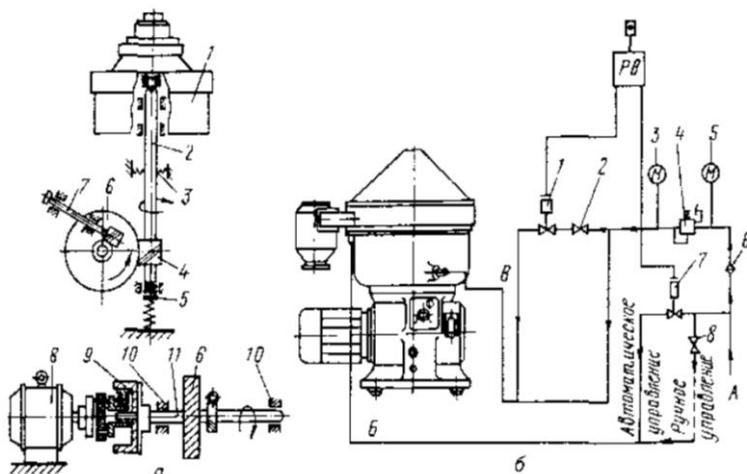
Схемы: а - принципиальная кинематическая сепаратора (1 – барабан, 2-вертикальный вал, 3 –упругая горловая опора, 4 -червяк, 5 –нижняя опора, 6 –червячное колесо;7-счетчик оборотов; 8- электродвигатель,9- муфта, 10- подшипники;11- горизонтальный вал),б- подключения гидросистемы сепаратора А – водопроводная вода избыточным давлением не ниже0,24 МПа, Б – вода для удаления осадка из приемника шлама: В-вода для подпитки при автоматическом или ручном управлении и для автоматического управления открытияи закрытия барабана, РВ- релевремени,1,7 –электромагнитные клапаны, 2, 8 – вентили, 3,5-манометры, 4-редуктор, 6-фильтр)
